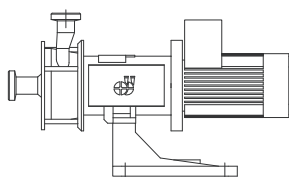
GEA Hilge CONTRA ADAPTA auf Gussfuß
